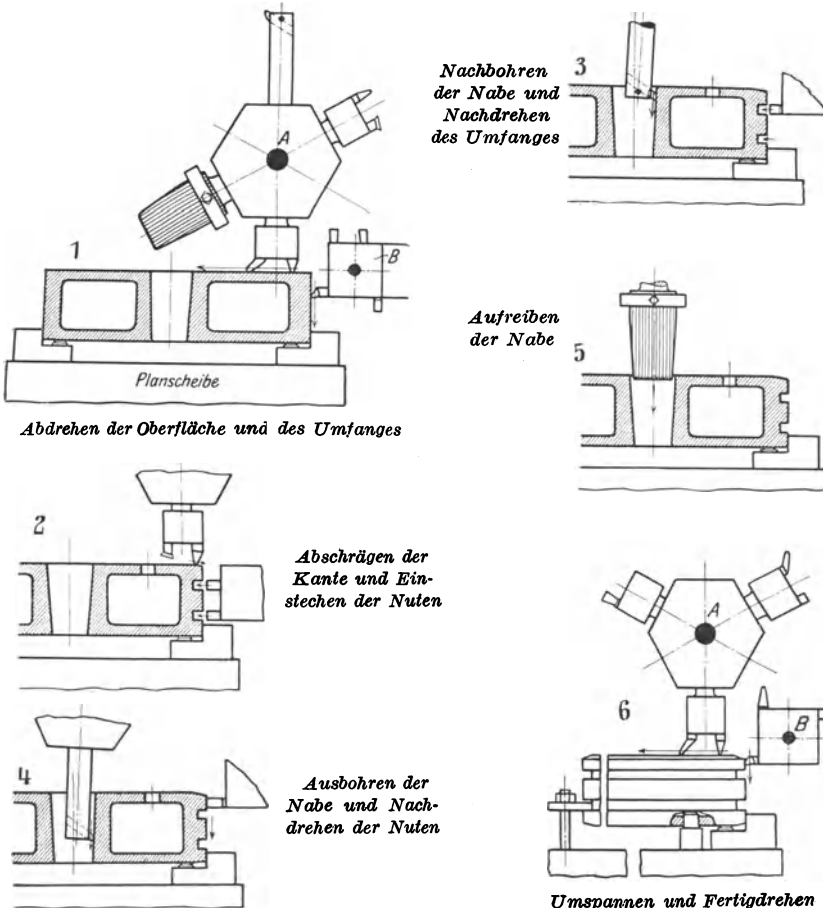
Bearbeiten eines Kolbenkörpers auf einem Dreh- und Bohrwerk.
